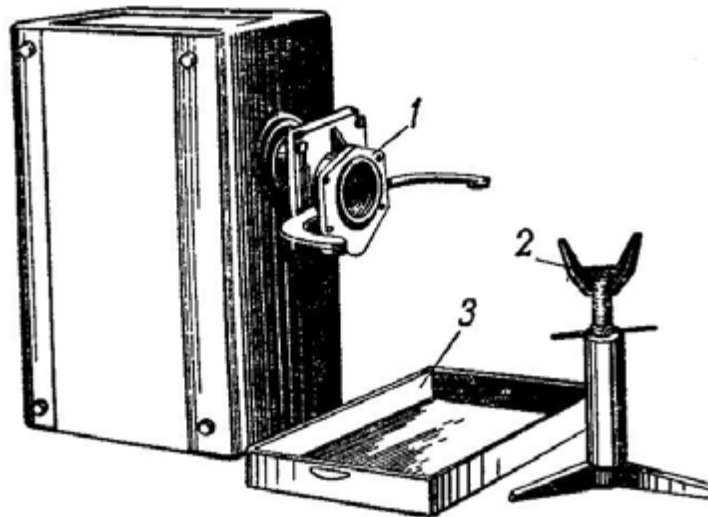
Стенд Р-235 для розбирання двигунів: 1 – шпindelь; 2 – підставка; 3 – піддон.
